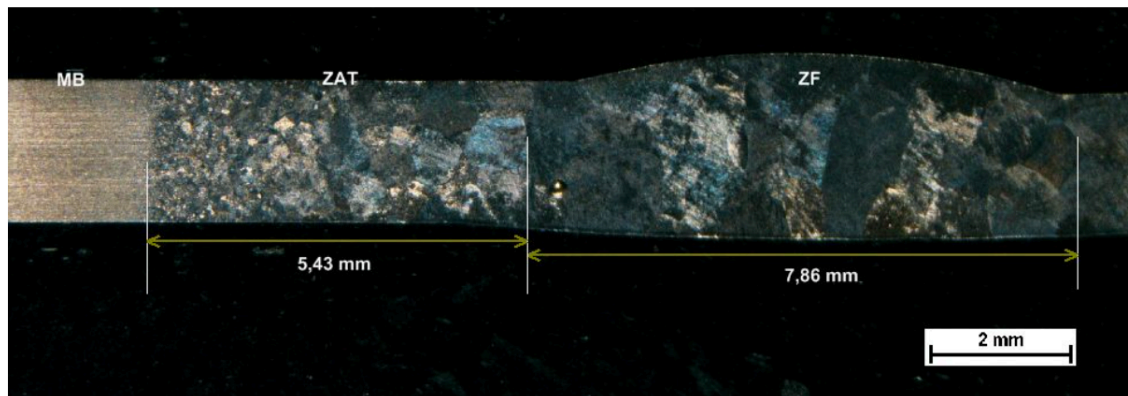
Macrographie d'une soudure avec un courant pulsé
